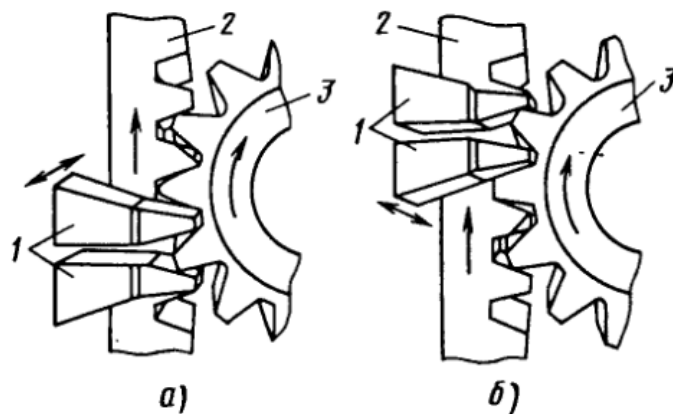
Схема нарізання конічних зубчатих коліс з прямими зубами двома зубостругальними різцями методом обкатування
